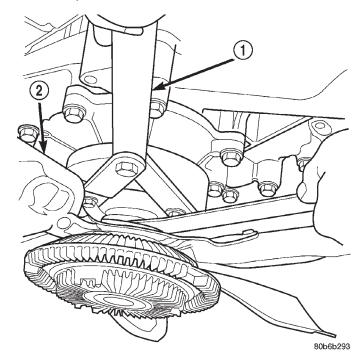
Ventilador y transmisión viscosa del ventilador del motor 3.7L
